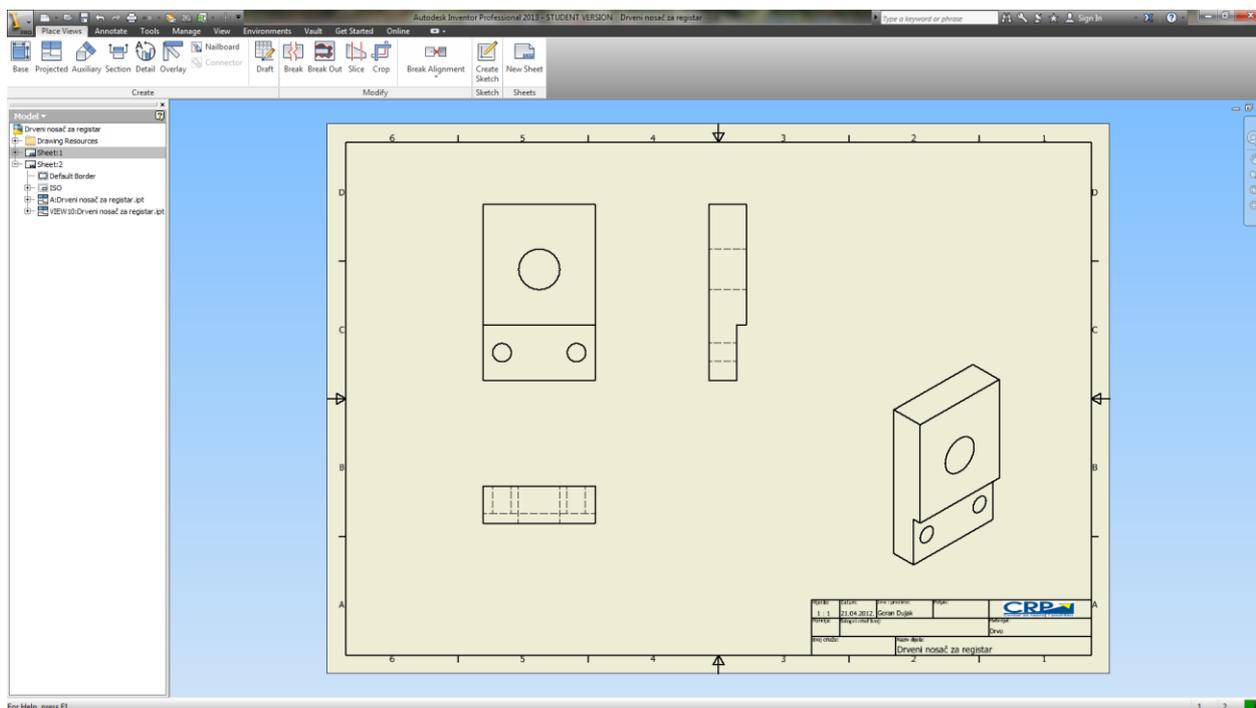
Izgled prozora za odabir pogleda crteža – *Drawing View
